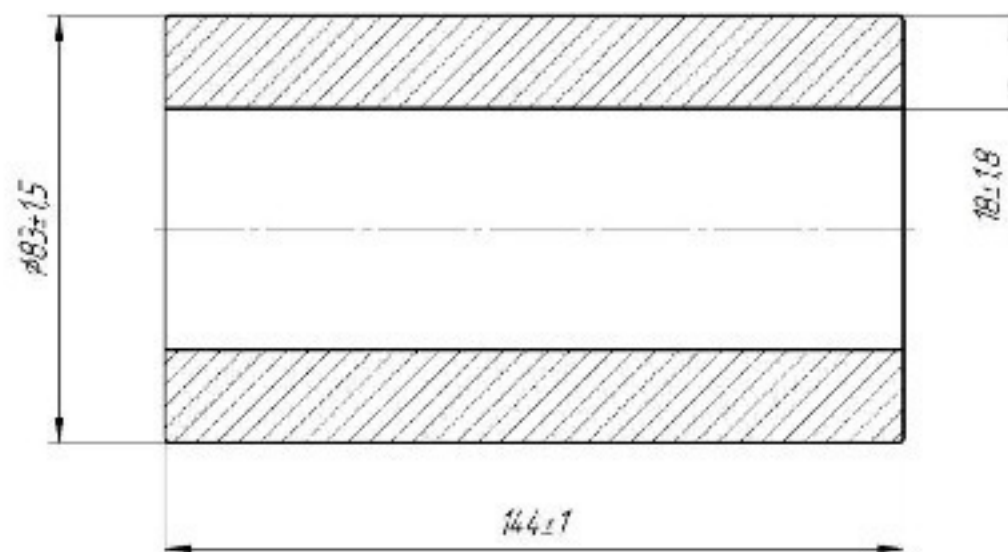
Ескіз заготовки виготовленої з трубного прокату
